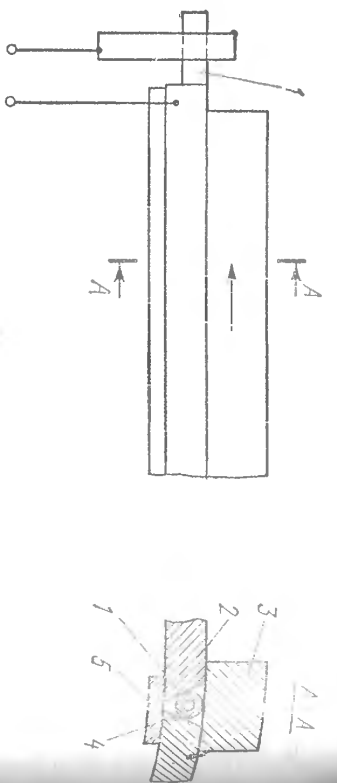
Схема сварки лежащим электродом:
